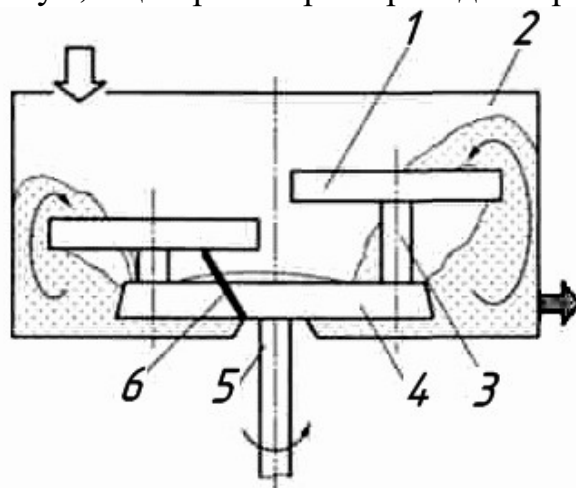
Центробежный, или маятниковый, смеситель: 1 – каток; 2 – чаша; 3 – кривошип; 4 – ротор; 5 – приводной вал; 6 – плужок
